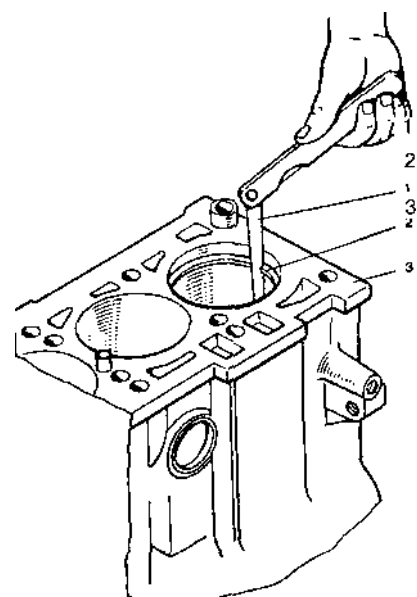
Проверка зазора в замке поршневого кольца: 1 — щуп; 2 — поршневое кольцо, 3 - блок цилиндров.
